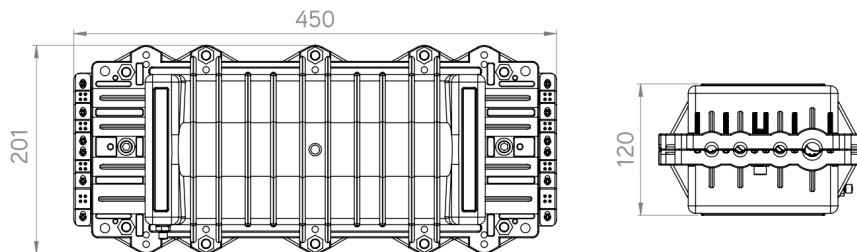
Vista exterior. Detalle de las vistas frontal y lateral con las dimensiones establecidas en mm.
